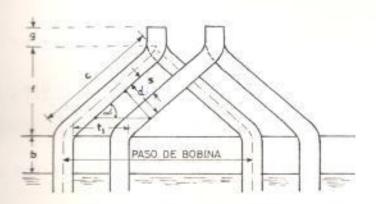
6 CABEZAL DE BOBINA DE ARMADURA
